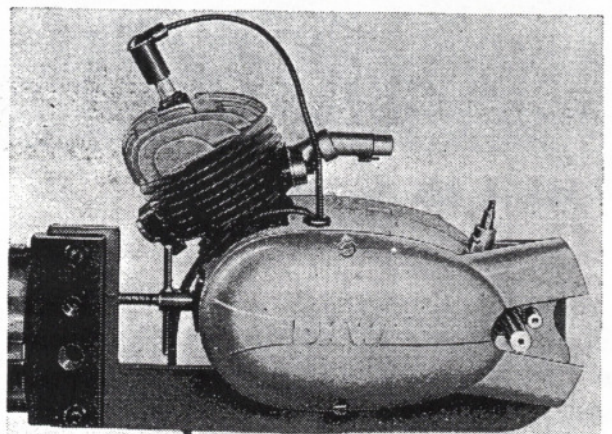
Motor kpl. am Aufnahmearm im Universal-Montagebock festgespannt VI/57/634
